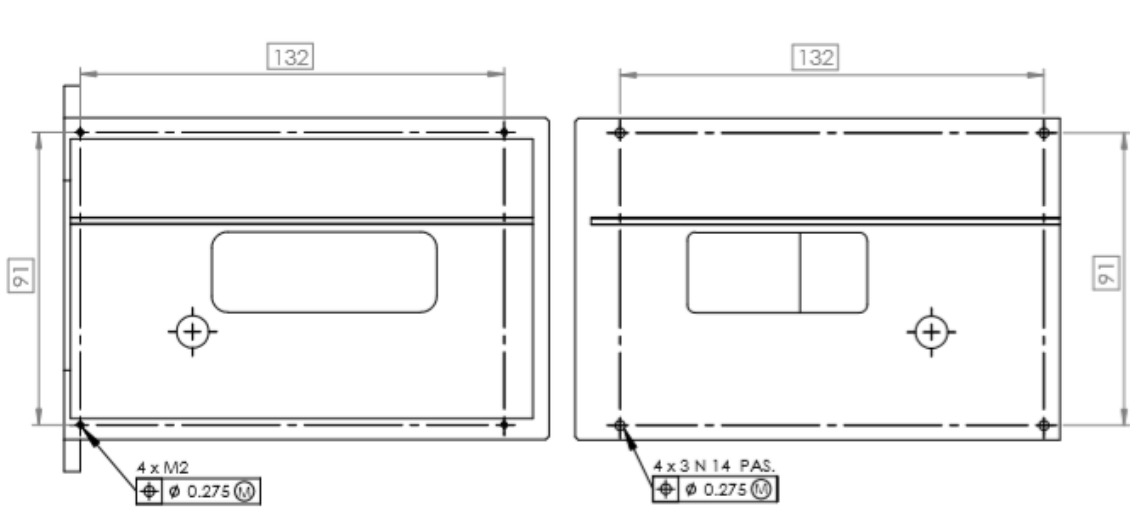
Representación de la tolerancia de posición para los taladros de la tapa izquierda y derecha.
